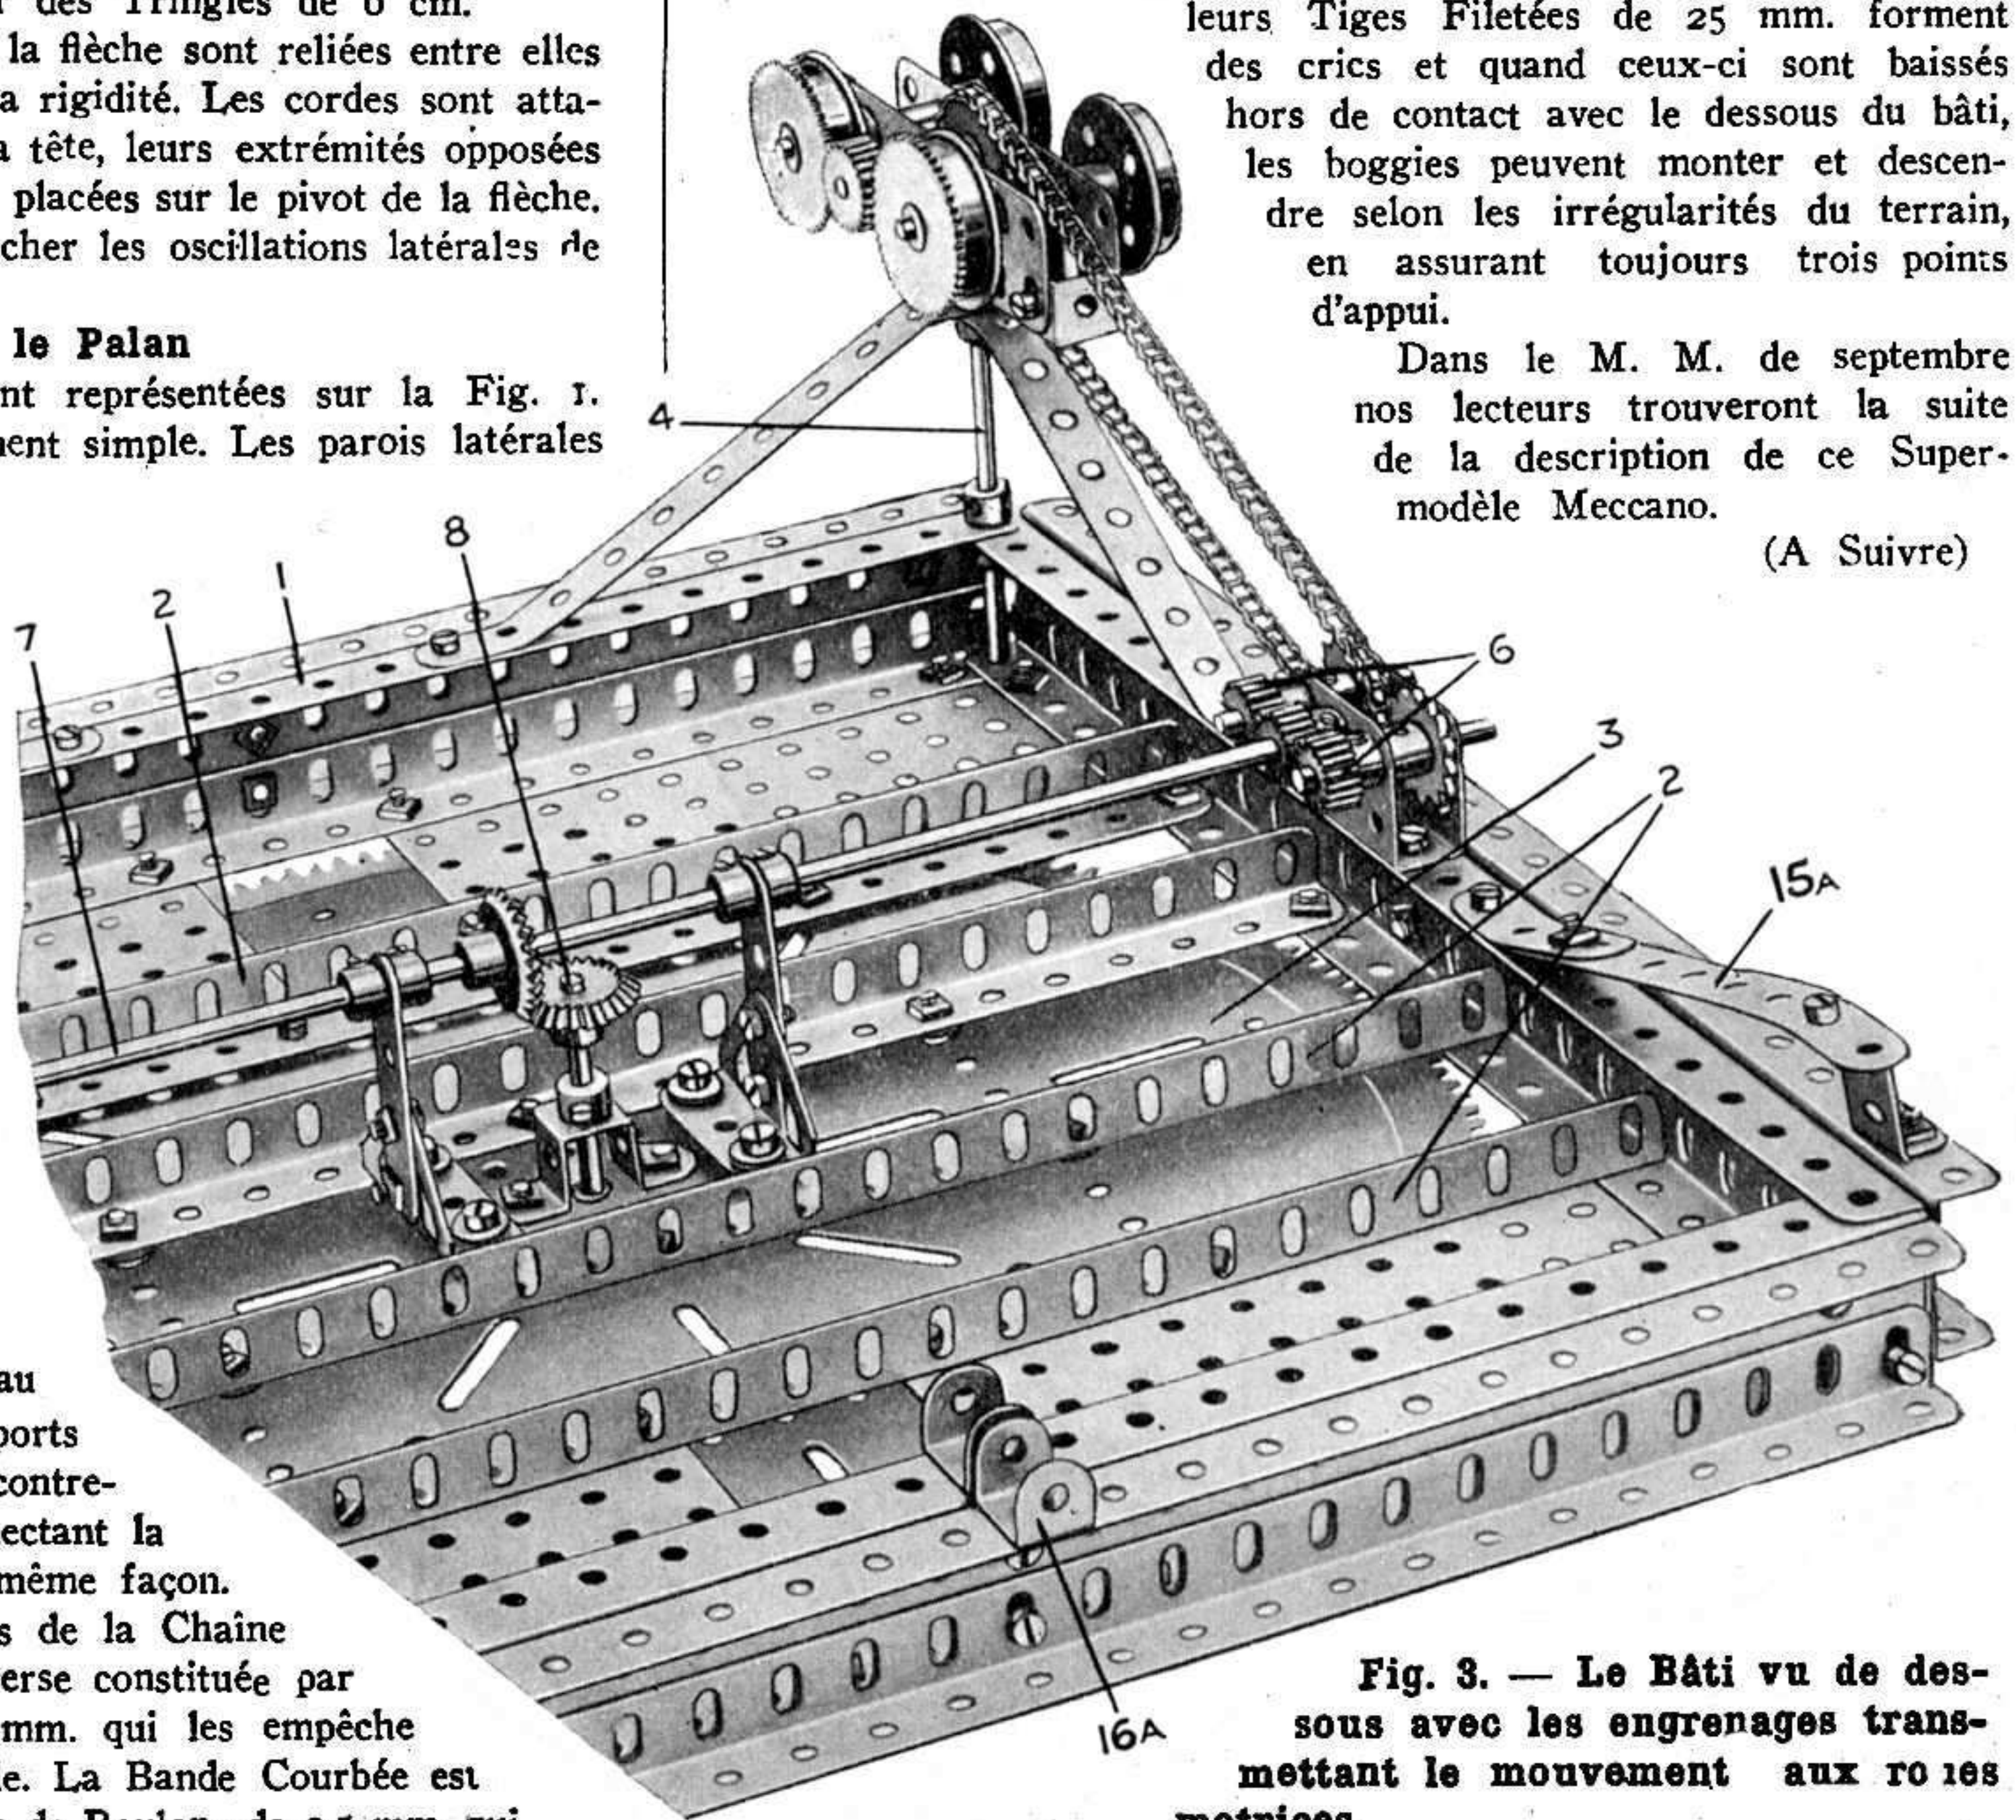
Le Bâti vu de dessous avec les engrenages transmettant le mouvement aux roues motrices.
